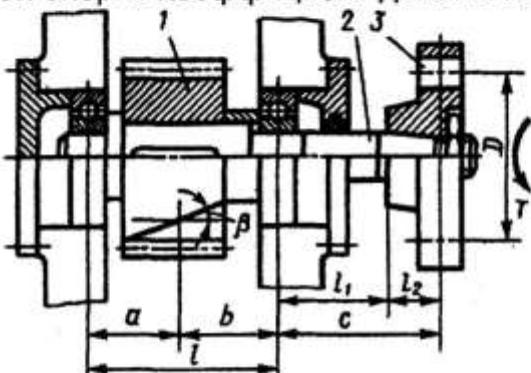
Вал с элементами, расположеннымными на нем: 1 – шестерня; 2 – вал; 3 – полумуфта
